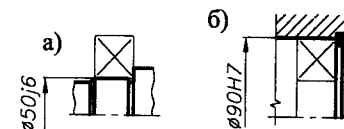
Обозначение посадок мест под подшипники: а) на валу; б) в отверстии корпуса
